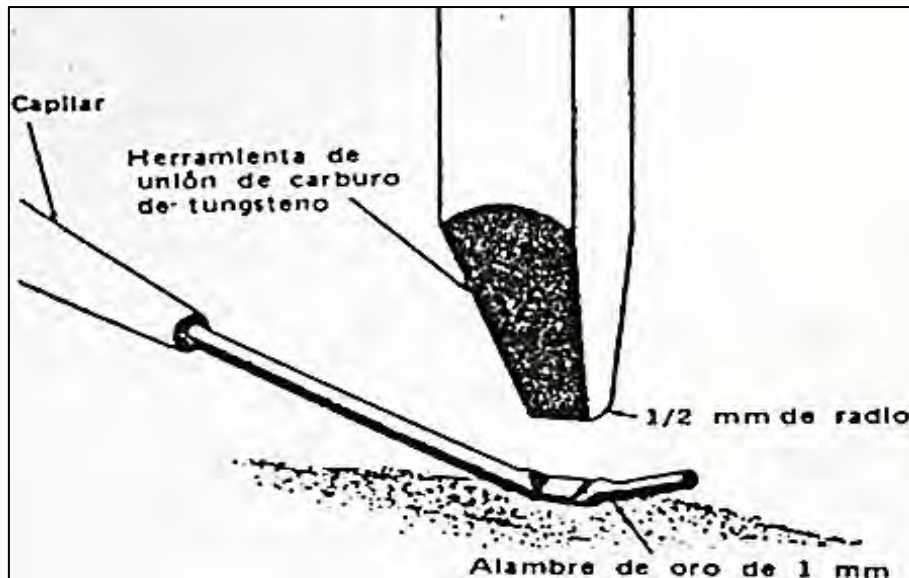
Soldadura empleada en circuito impreso [22].
